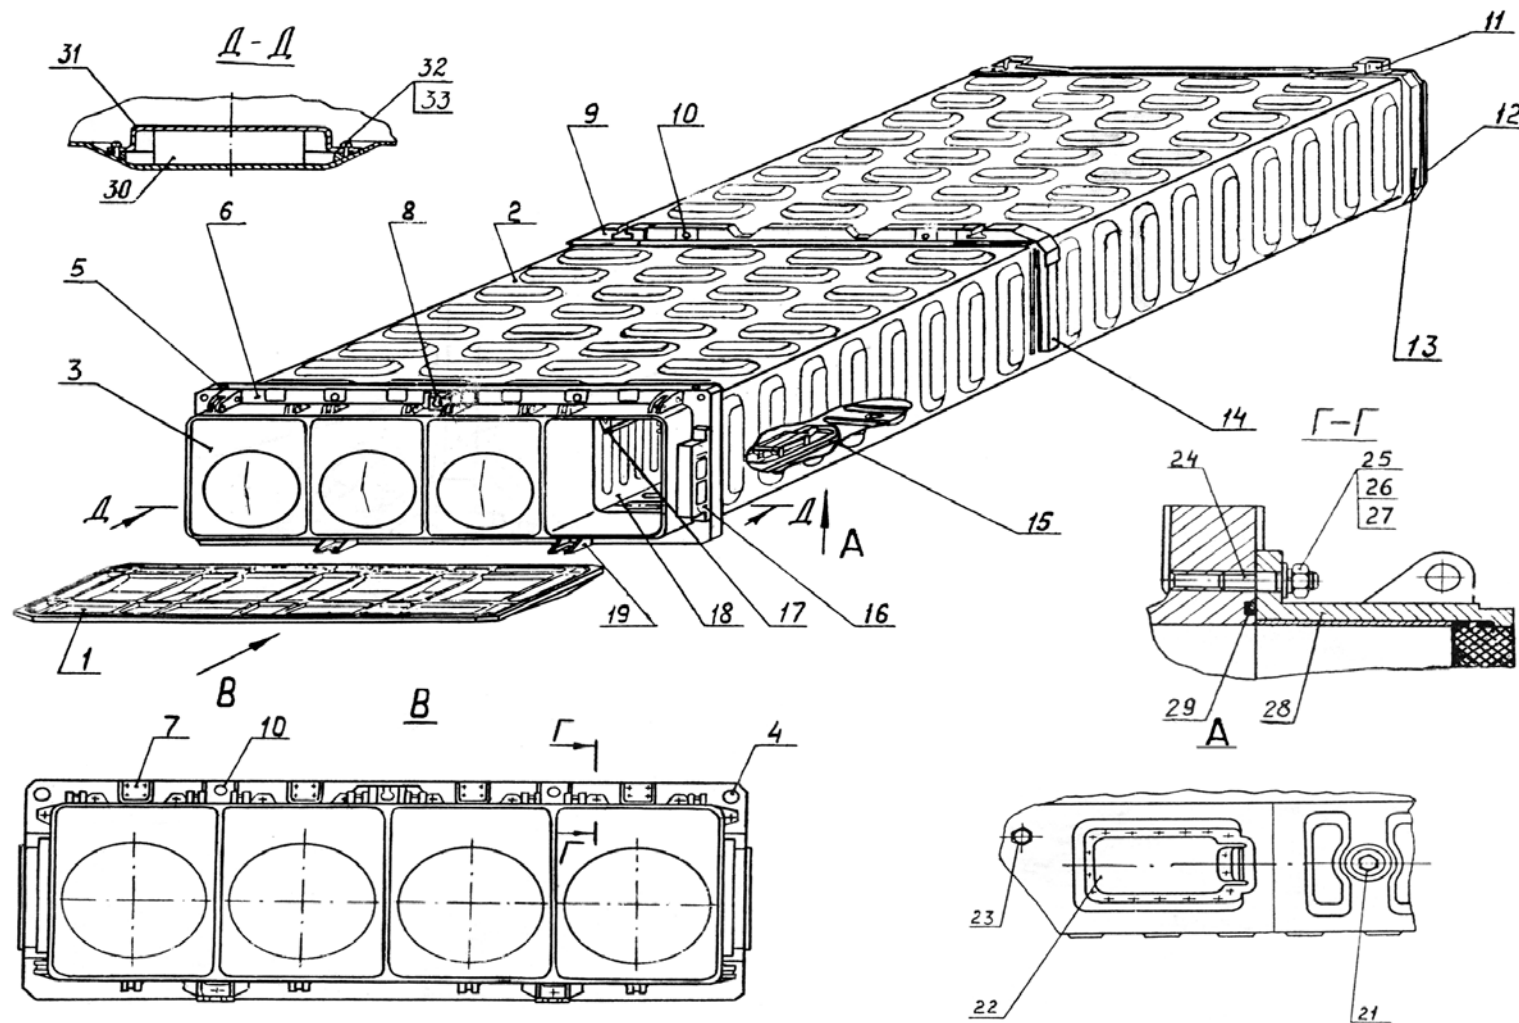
Транспортно-пусковой контейнер: 1 – крышка передняя; 2 – корпус; 3 – крышка разрушающаяся; 4 – отверстие; 5 – гнездо; 6 – шпангоут передний; 7 – пластина; 8,19 – кронштейн; 9 – бугель передний; 10 – узел подъема; 11 – бугель задний; 12 – крышка задняя; 13 – шпангоут задний; 14 – шпангоут средний; 15 – механизм расстыковки электроразъема; 16 – электроразъем; 17 – балка направляющая; 18 – диафрагма; 20, 23 – пробка для продувки; 21 – пробка люка переключения литеры; 22 – крышка механизма расстыковки электроразъема; 24 – шпилька; 25 – гайка; 26,27,33 – шайба; 28 – ЗГУРД; 29 – прокладка; 30 – осушитель (силикагель); 31 – крышка; 32 – винт
